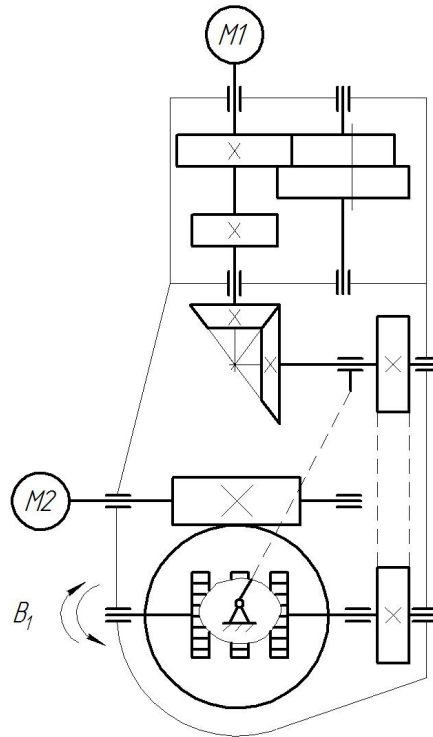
Кінематична схема фрезерної головки верстата для здійснення обробки в умовах РПВС
